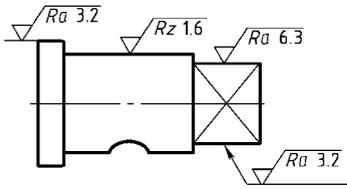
圆柱和棱柱的表面粗糙度轮廓
